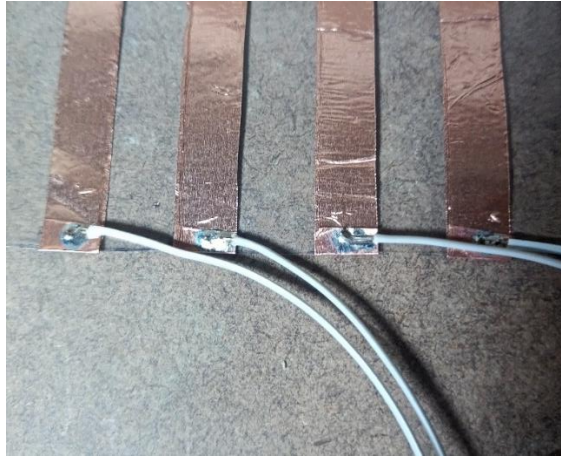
Soldadura del cableado de la matriz sensorial.
